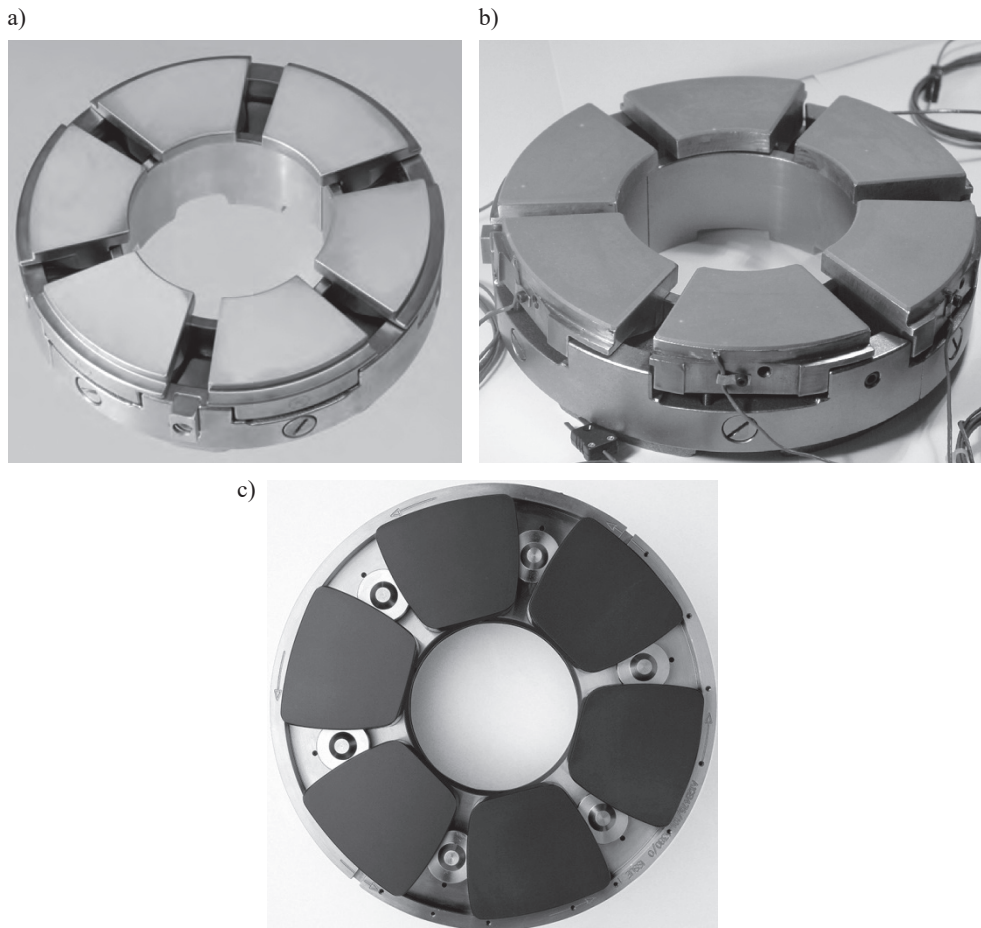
Segmenty łożysk wzdłużnych w ofercie Waukesha Bearings [227]:
